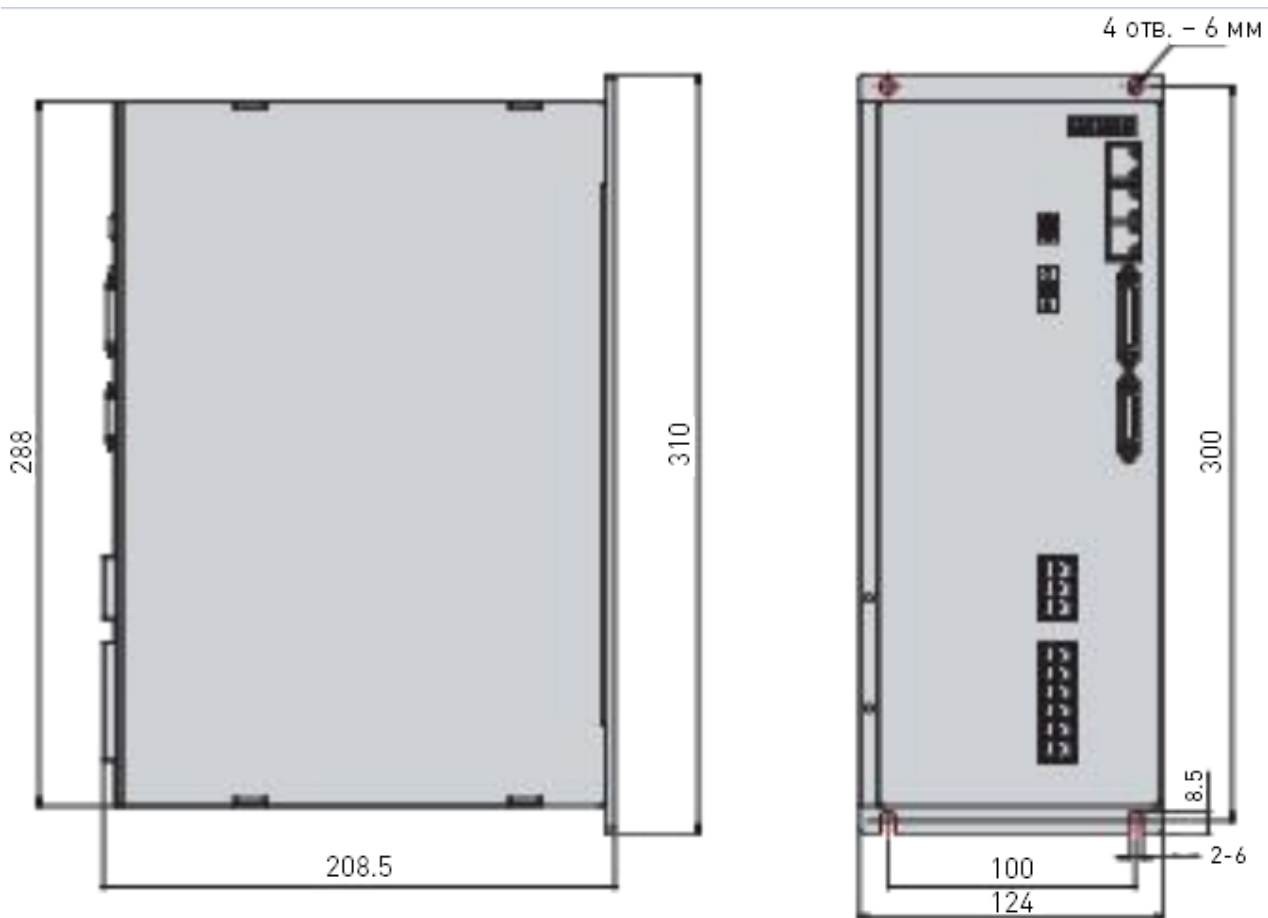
Габаритный чертеж драйверов ETD-A3024.
